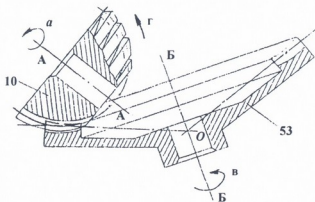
Схема нарезания конического колеса с внутренними зубьями
